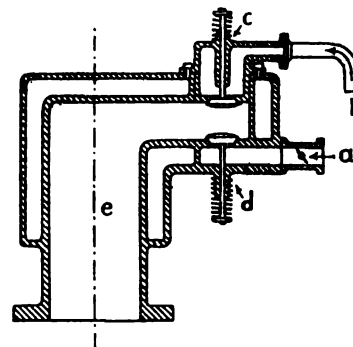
a) Regolazione - b) dal carburatore arrivo di aria carburata in eccesso - c) valvola di aspirazione di aria sopra carburata - d) idem normale - e) Cilindro motore.
